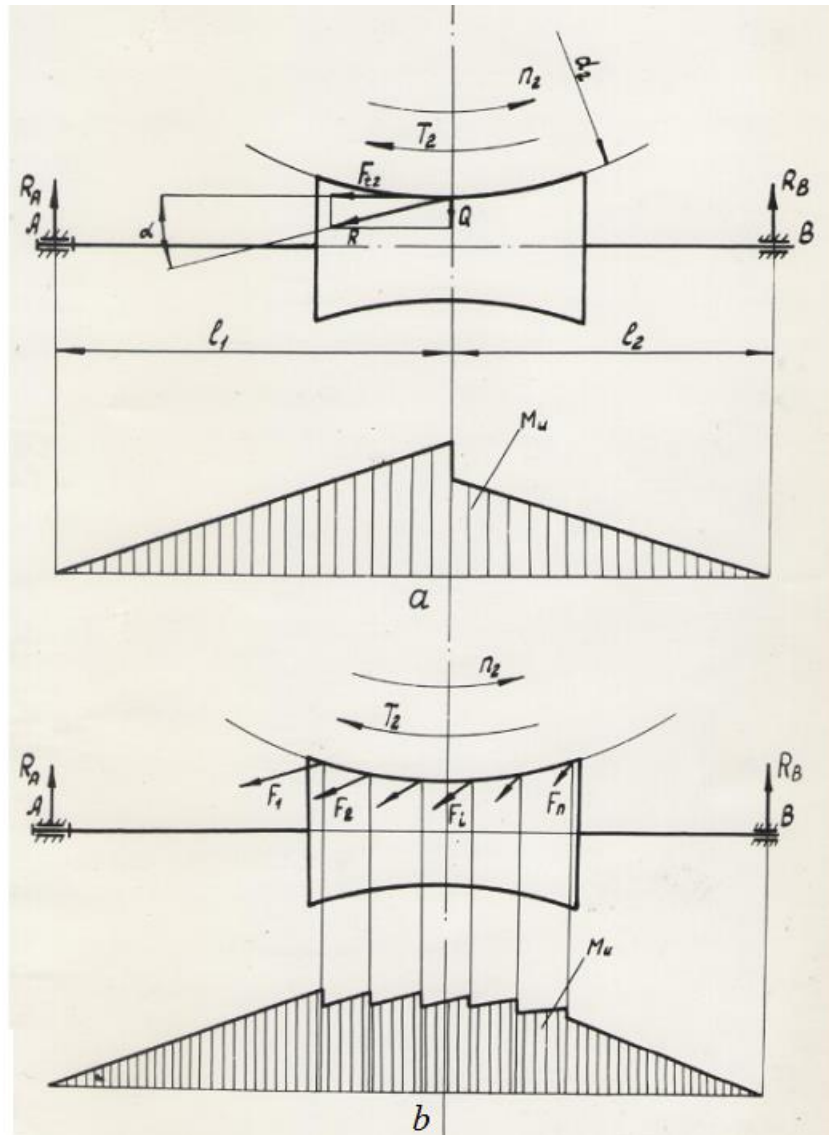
Розрахункова схема глобоїдного черв'яка.
